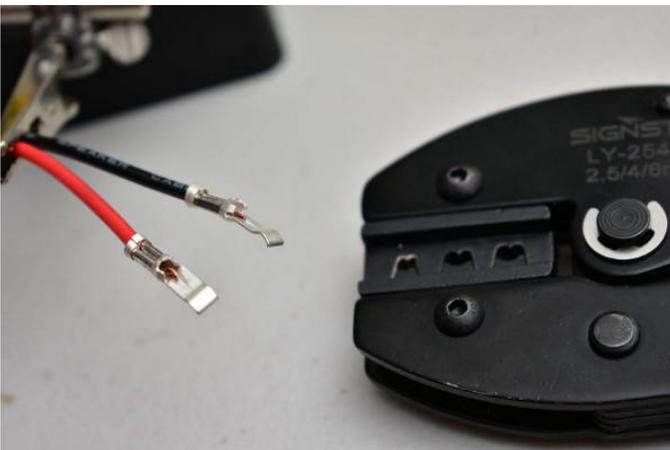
Añadí un poco de soldadura para una mejor conductividad
